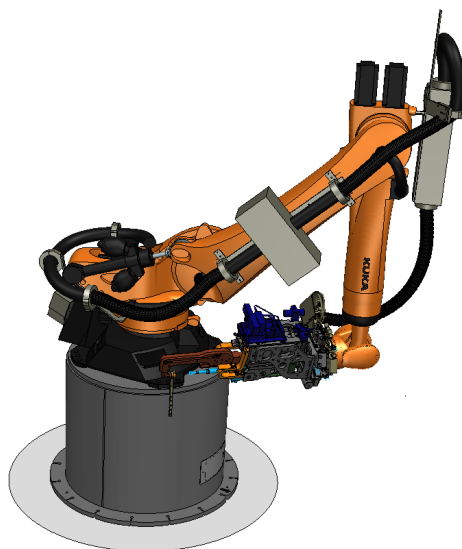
Положение для калибровки сварочного пистолета робота 5080R01 Z
